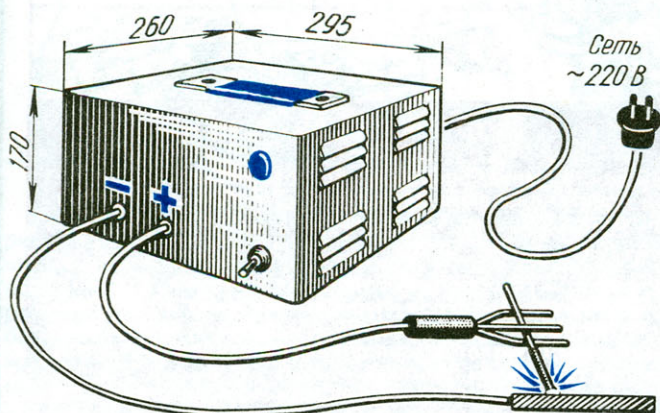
Самодельный аппарат для сварки на постоянном токе.
